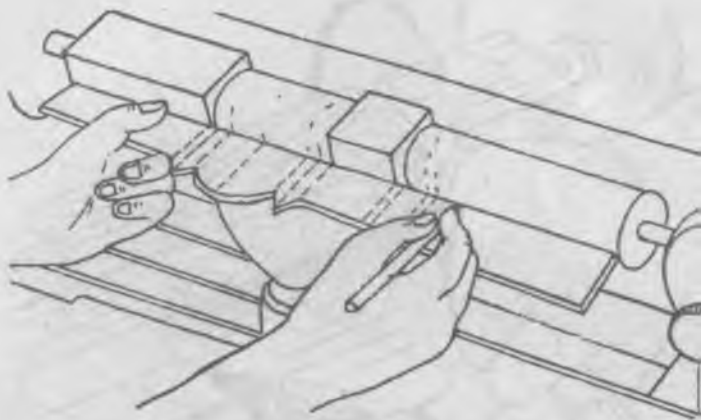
Проверка разметочных линий шаблоном в процессе обработки заготовки
